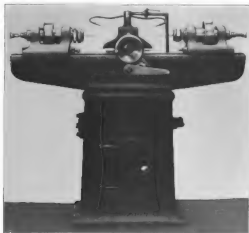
Bohrmaschine zur Herstellung der Stehbolzenbohrungen (Werkzeugmaschinenfabrik Ernst Schieß).
